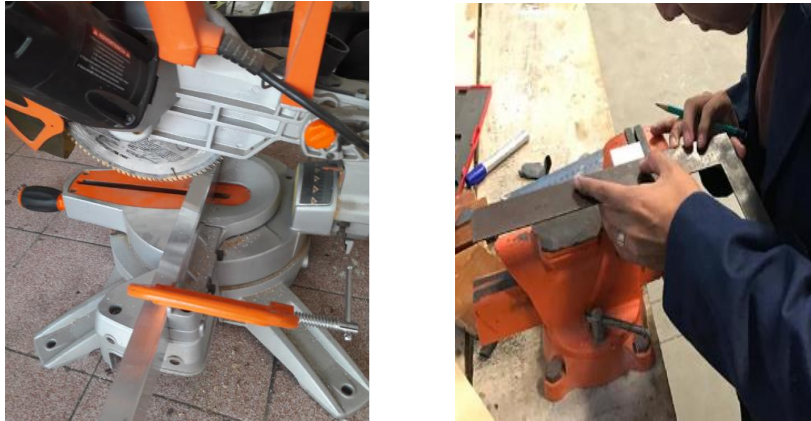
Corte de aluminio y trazado en piezas de aluminio.
